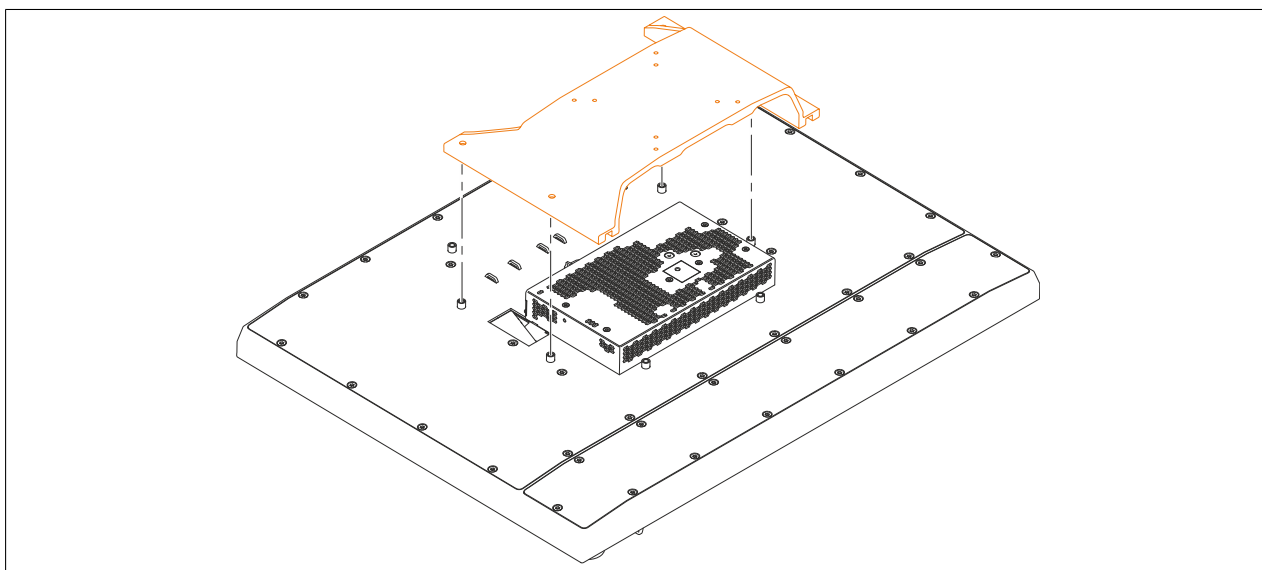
Konsole entfernen bzw. am Panel platzieren
